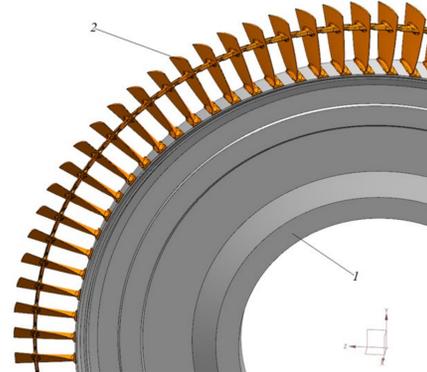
Конструкторская модель рабочего колеса 8 ступени, 1 – диск; 2 – рабочая лопатка
